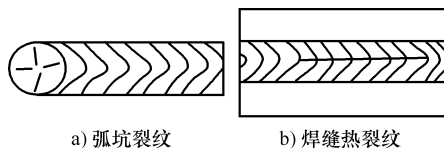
弧坑裂纹及焊缝热裂纹
